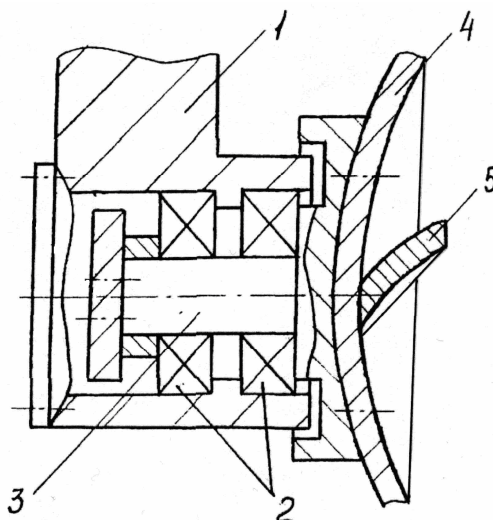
Новая конструкция дискового корпуса (патент №2253206)
